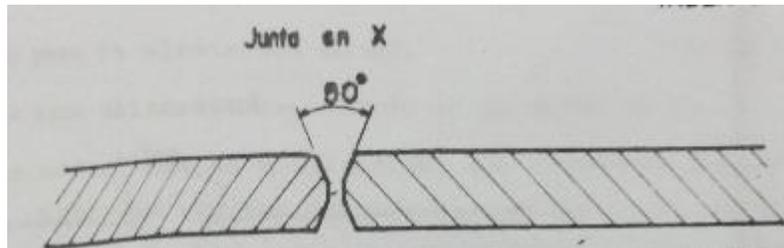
Formas de aplicar los cordones de soldadura
